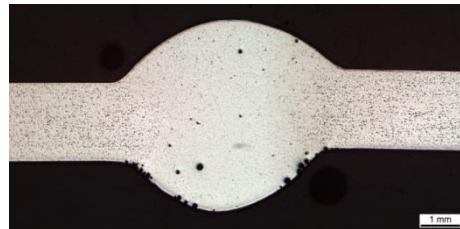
Микрошлиф сварного шва, $V = 4$ м/мин
